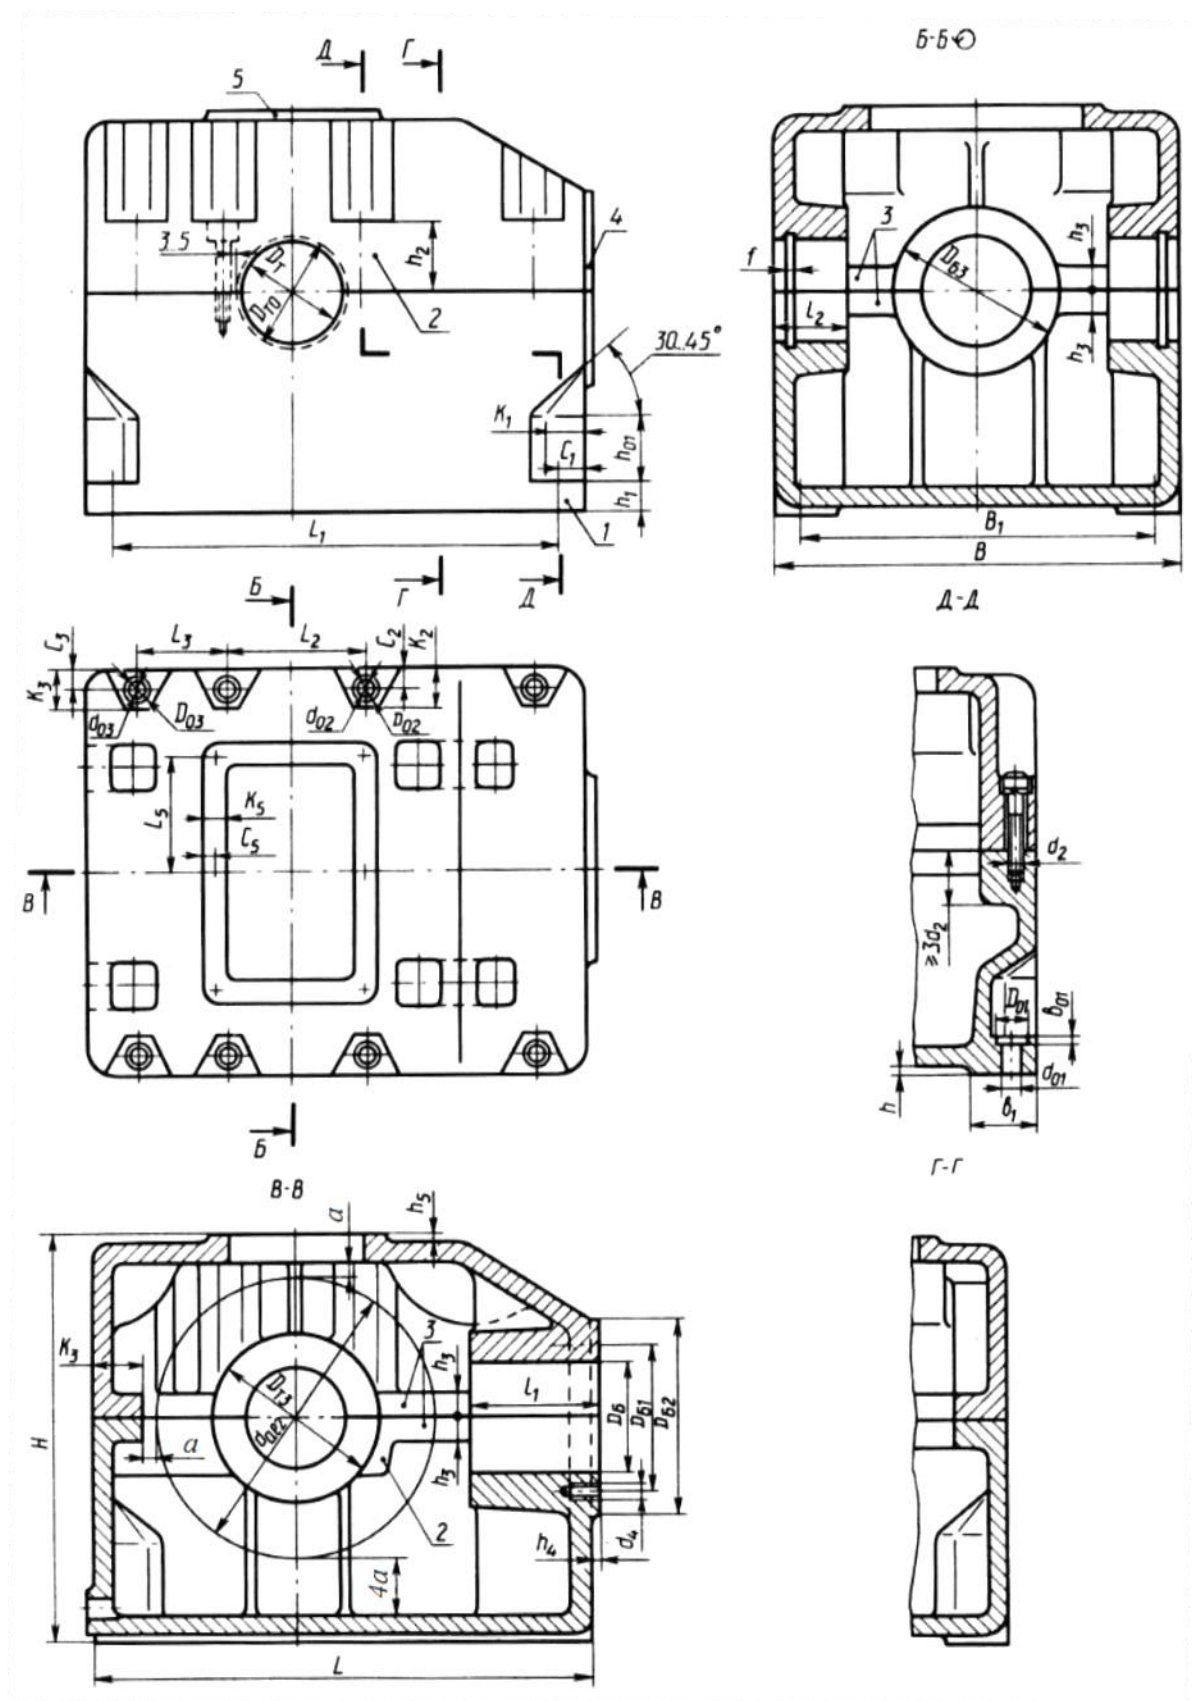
Разборный корпус одноступенчатого горизонтального конического редуктора
